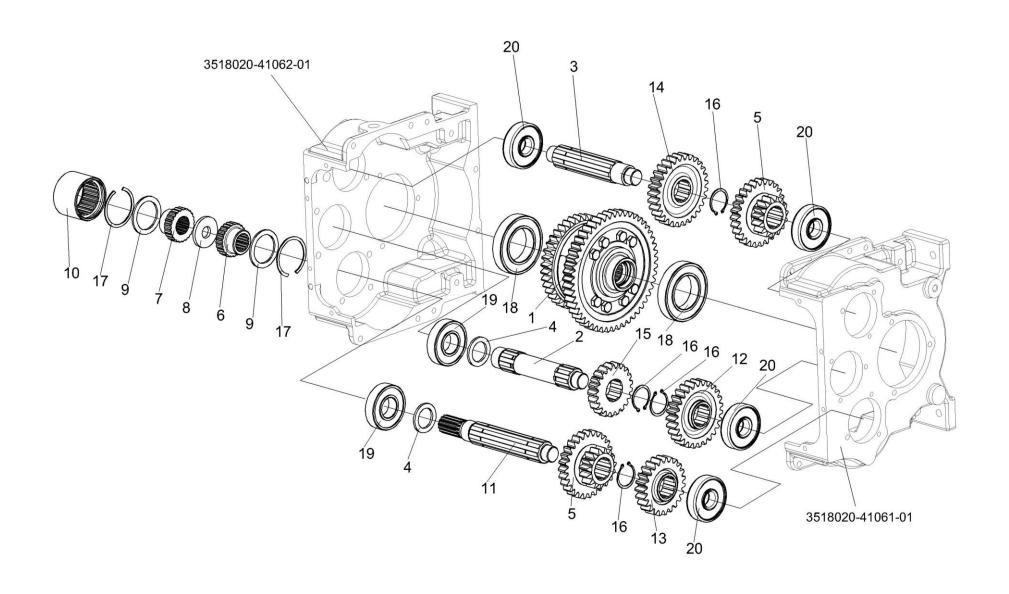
Коробка диапазонов 3518020-46150 (валы, шестерни)
